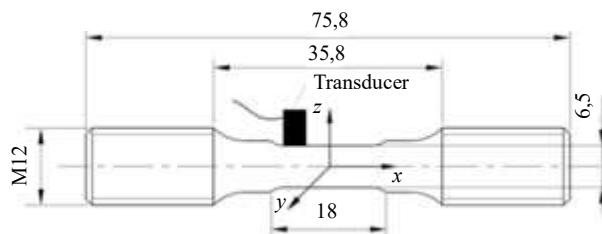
Форма образца для усталостных испытаний и схема установки преобразователей
